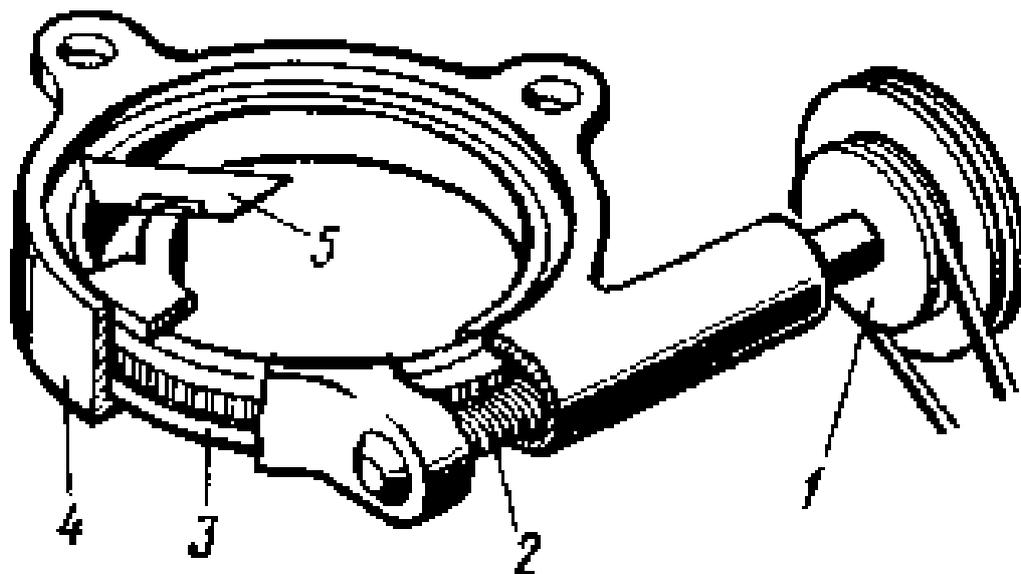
Режущий механизм конструкции И. М. Певнего:
